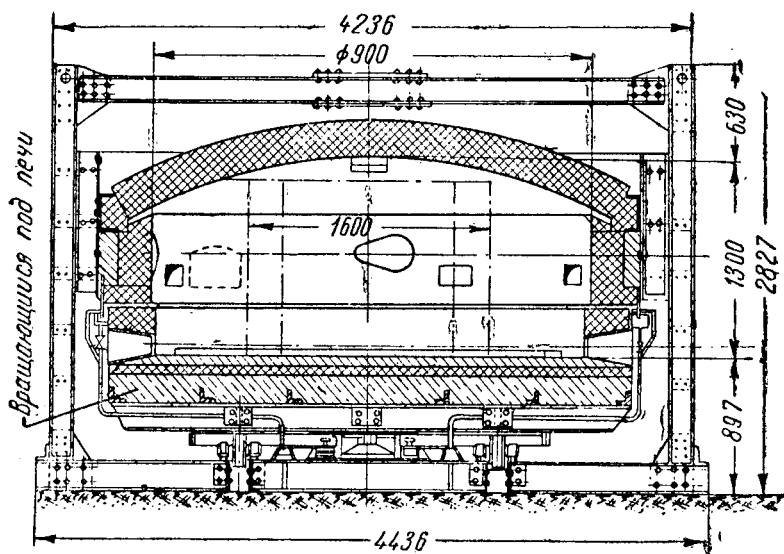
Печь с регенераторами для нагрева крупных слитков
